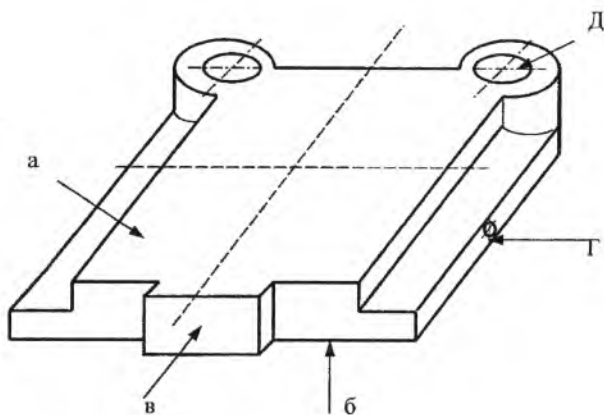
Нижняя плита штампа из исходной литой заготовки
